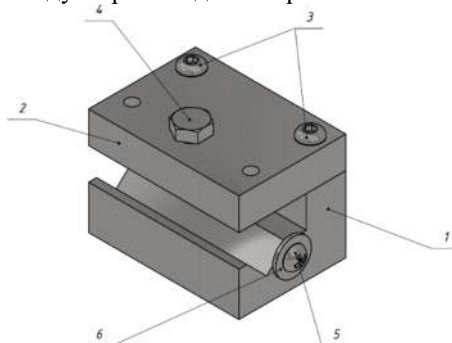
Зовнішній вигляд кондуктора: 1 – базова деталь, 2 – кришка, 3 – гвинти, 4 – затискний болт, 5 – гвинт закріплення упору, 6 – шайба-упор.
